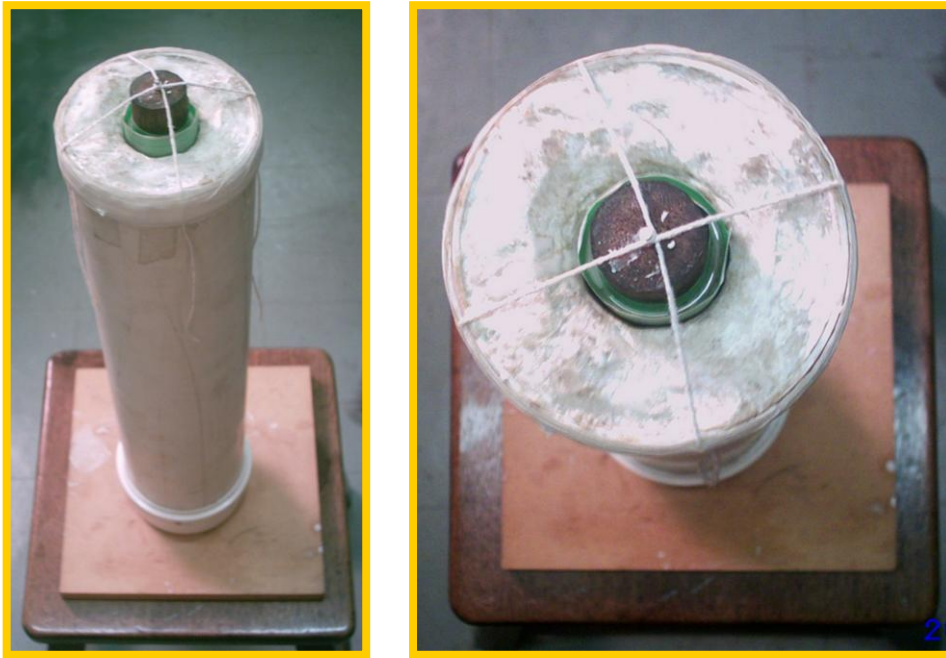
Detalhes do molde de gesso utilizado na confecção do tubo de silicone
